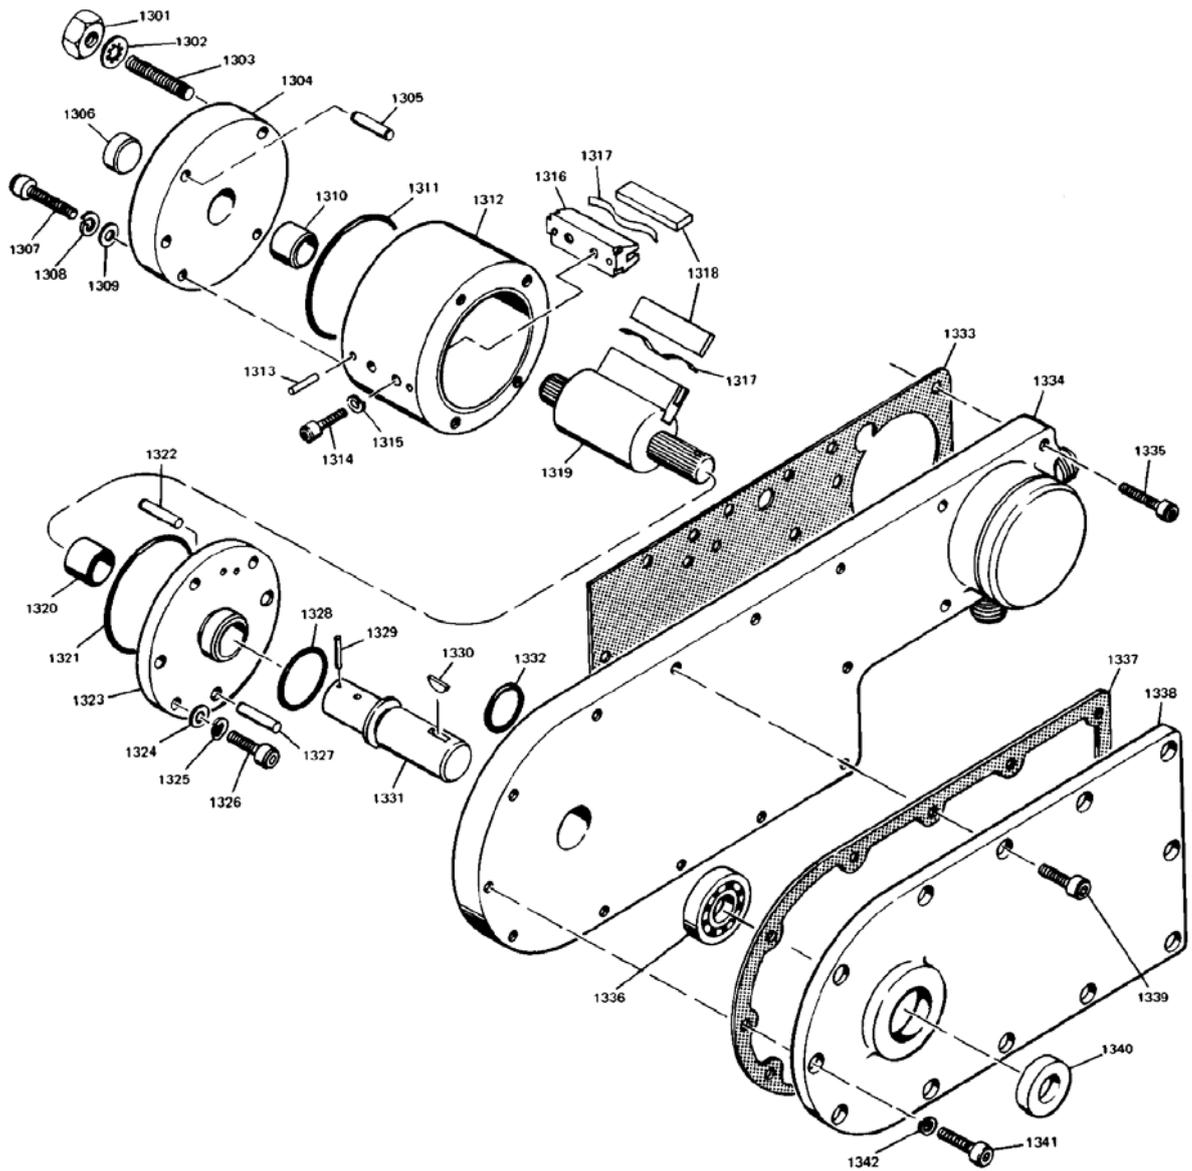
Покомпонентный чертеж встроенного лопастного сервопривода
